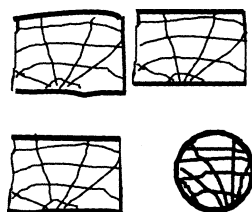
Варіанти форм поперечного перетину заготовок перед гнуттям: А - після розкрою; Б - перед гнуттям
